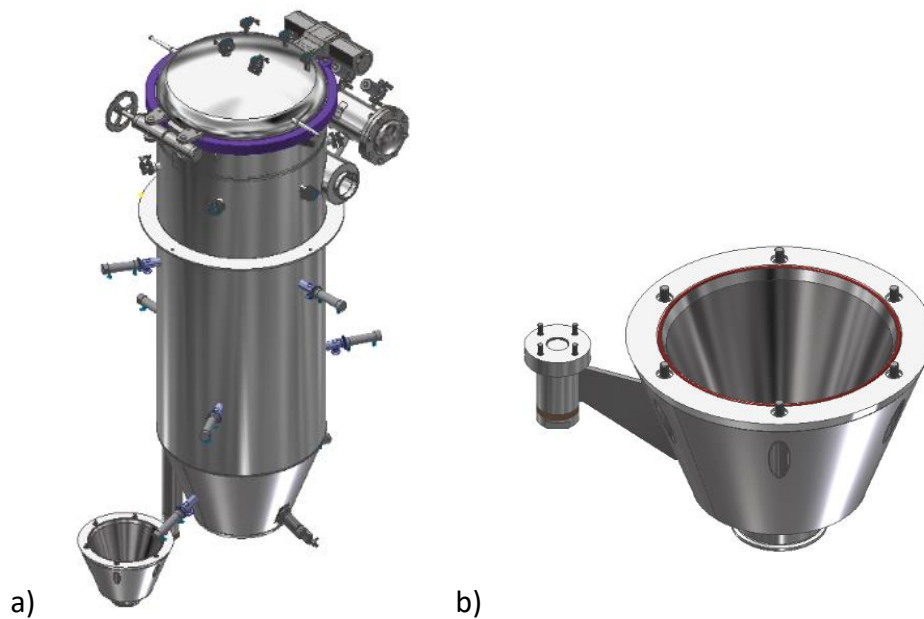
Bag filter* atualizado: a) Instalação do cone de inspeção; b) Cone de inspeção
